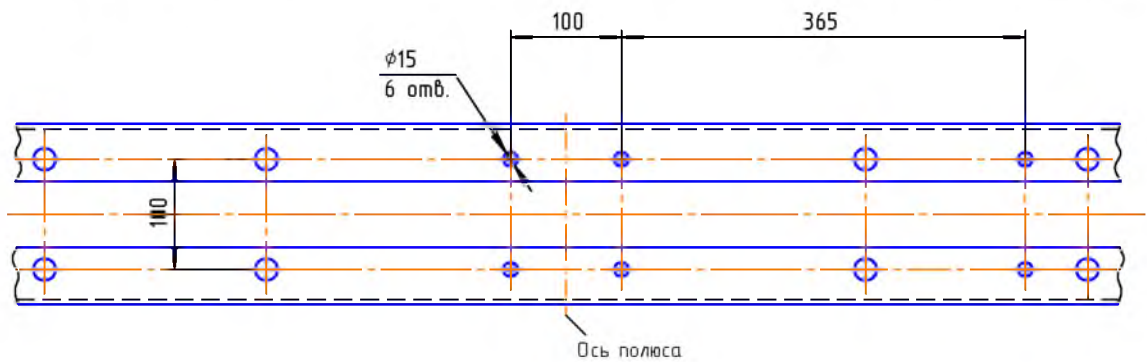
Разметка отверстий для присоединения рамы к полюсу разъединителя
